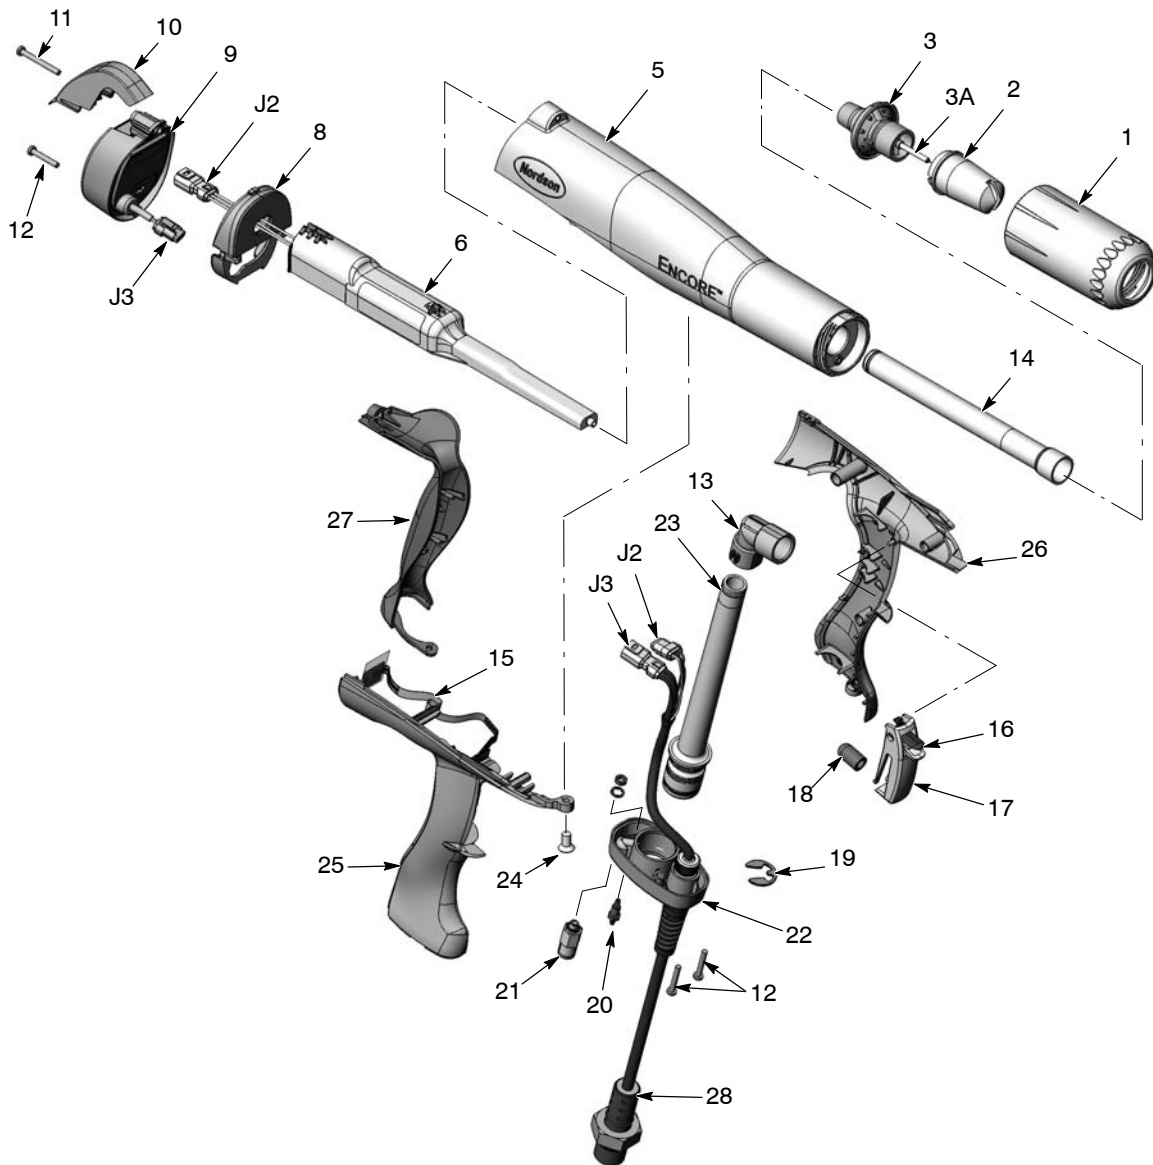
Explosionszeichnung der Sprühpistole (Nummerierung wie in der Ersatzteilliste)
